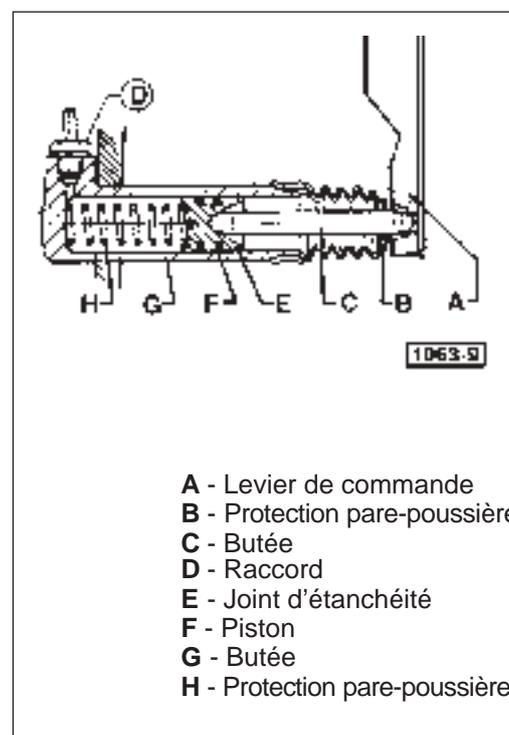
Coupe du cylindre de commande d'embrayage.
